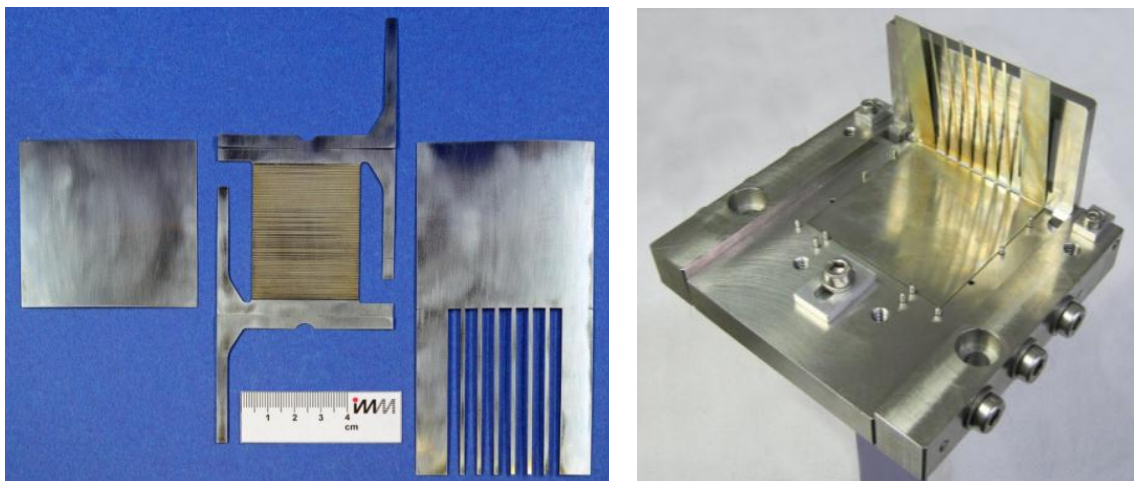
Trenn-, Reformier- und Kreuzstromblech (l.); Biegewerkzeug (r.)
